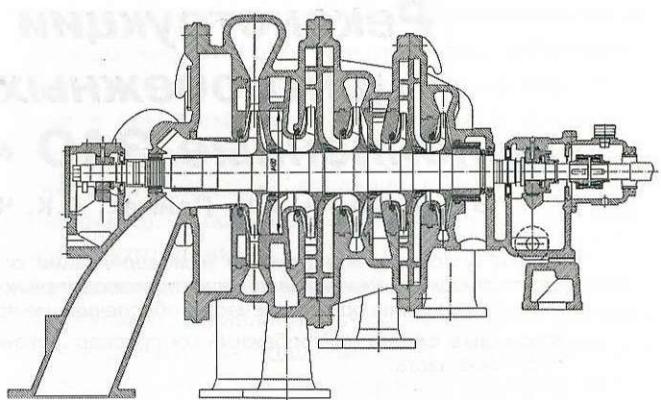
Продольный разрез реконструированного компрессора К 250-61-1
